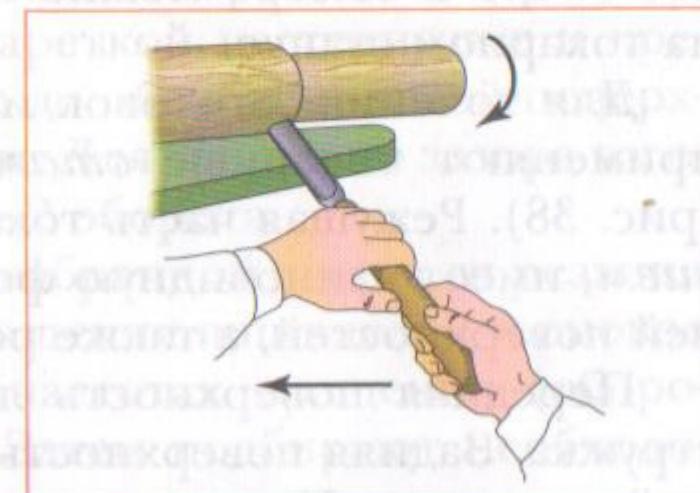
Приём продольного точения на токарном станке; придание заготовке цилиндрической формы.
